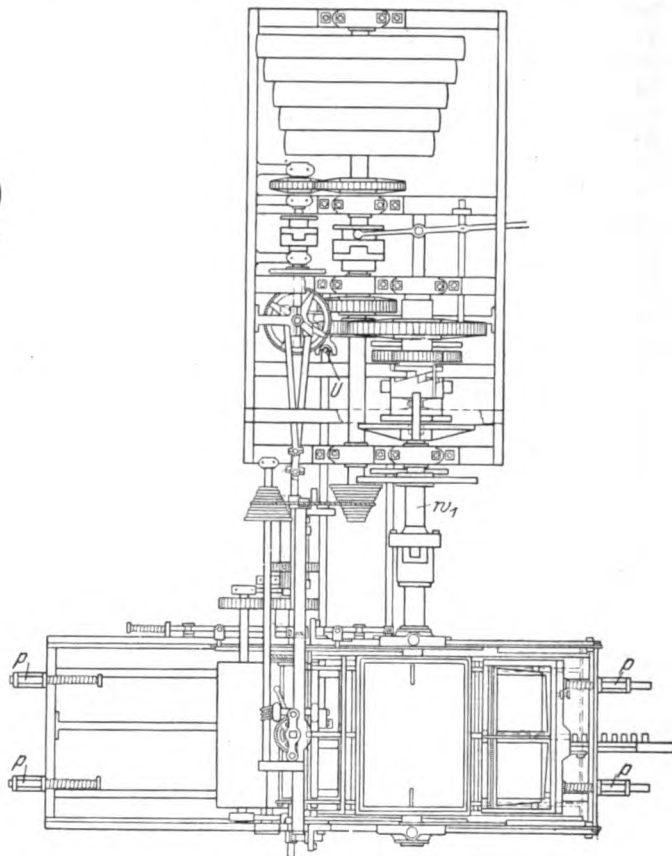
Erste Zylinderdruckmaschine, Grundriß
